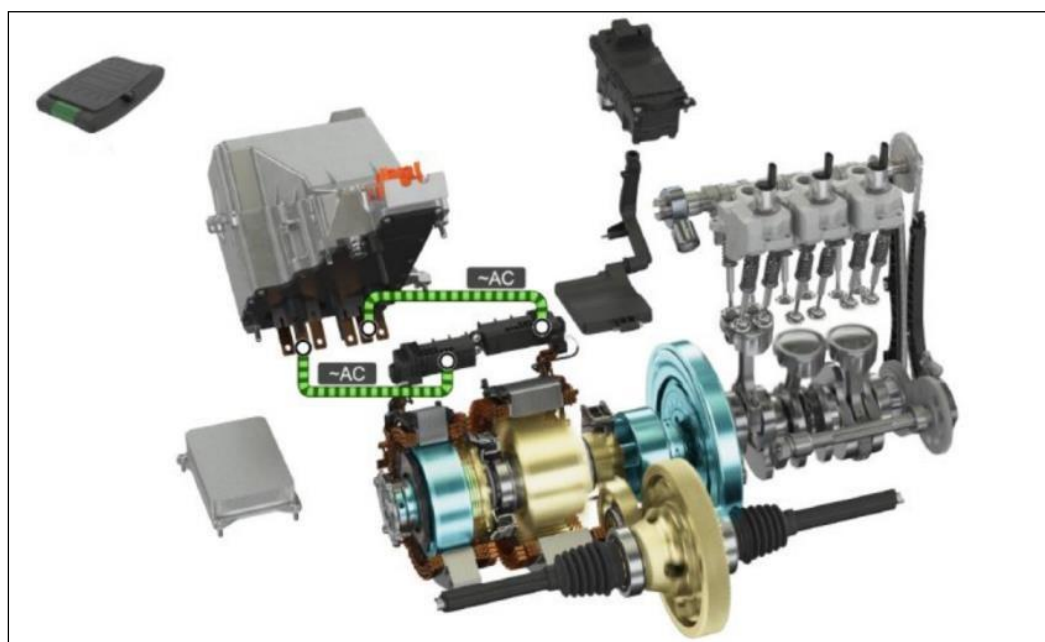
Motor elétrico 01 fornece propulsão para as rodas e motor a combustão utiliza o motor elétrico 02 para geração de energia.
